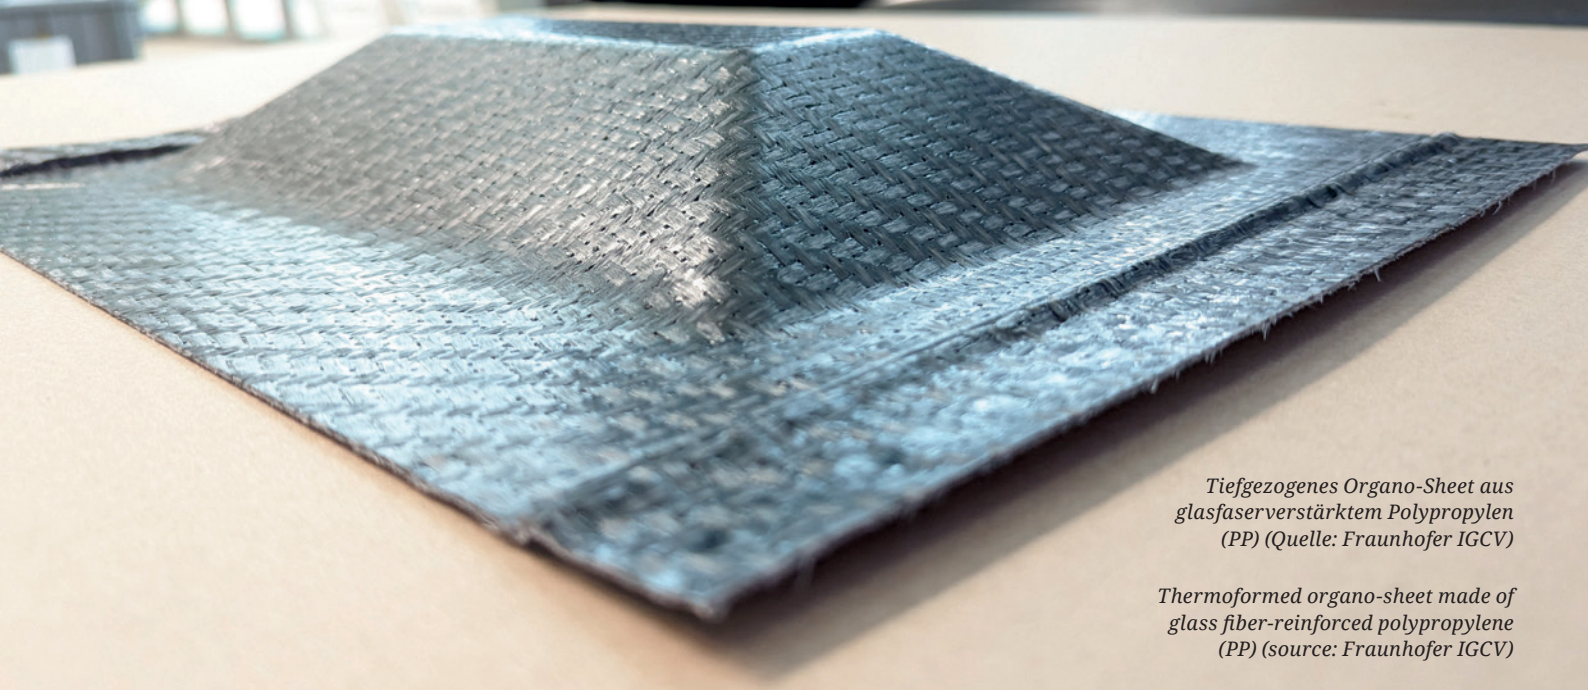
Thermoforming eines PP-Sheets auf dem entwickelten Prüfstand (Quelle: Fraunhofer IGCV)
